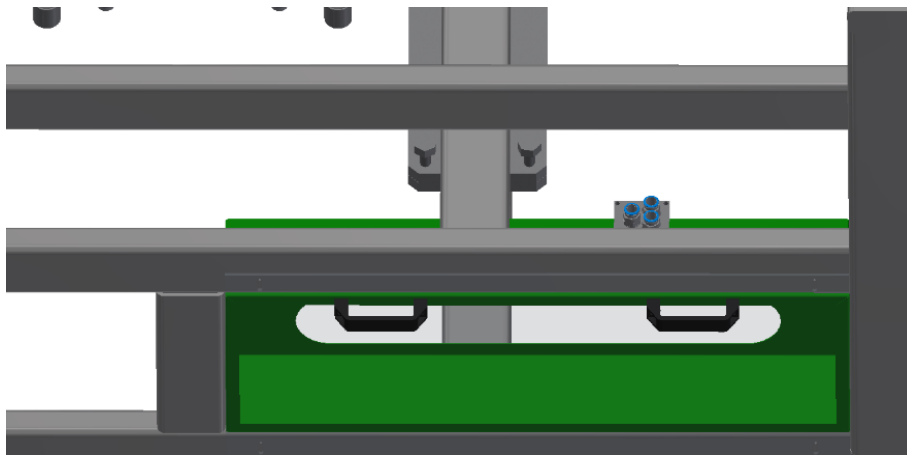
Compartimento soldado ao subconjunto 011 - Estrutura principal
